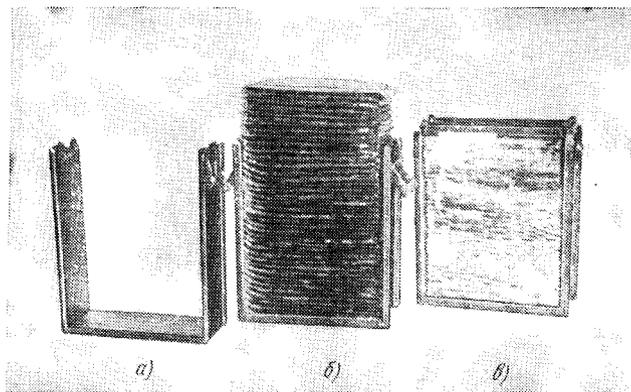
Сборка пакетов конденсатора ЭСВ:
